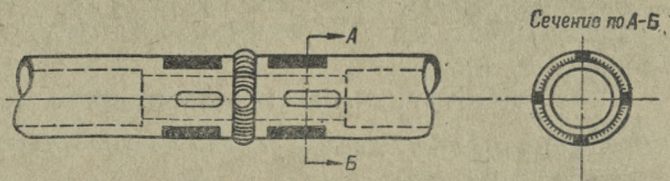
Увеличение длины сварного шва на трубчатой конструкции при помощи прорезей
